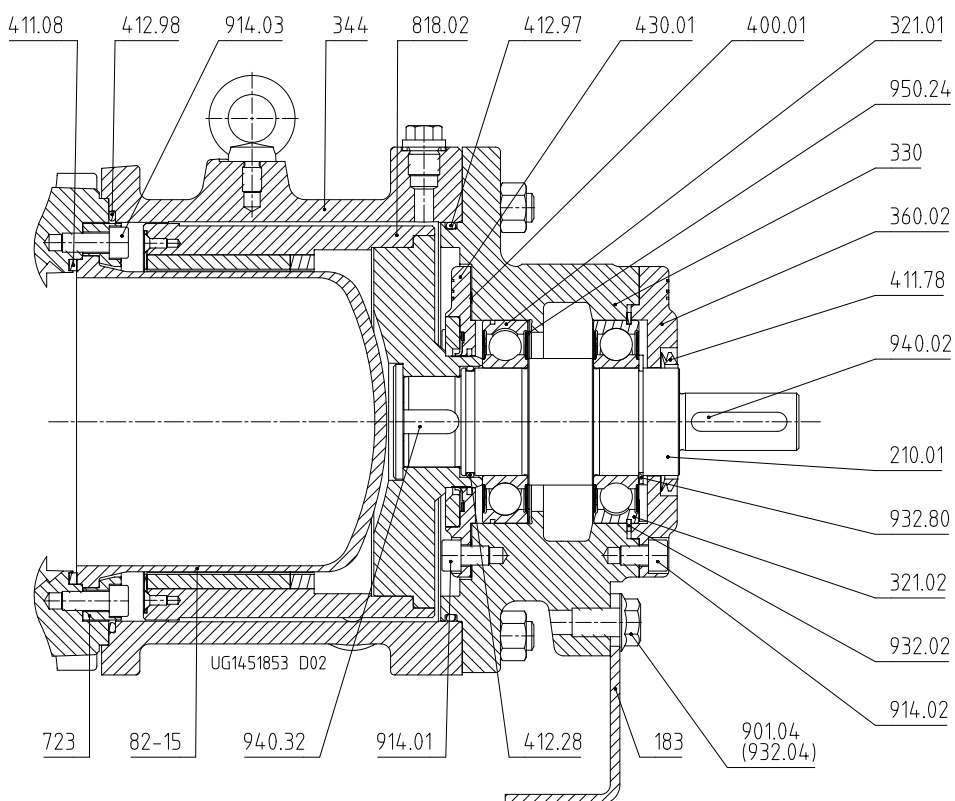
Крепление крышки корпуса с напорной стороны на корпусе насоса для исполнения с зажимной крышкой корпуса
